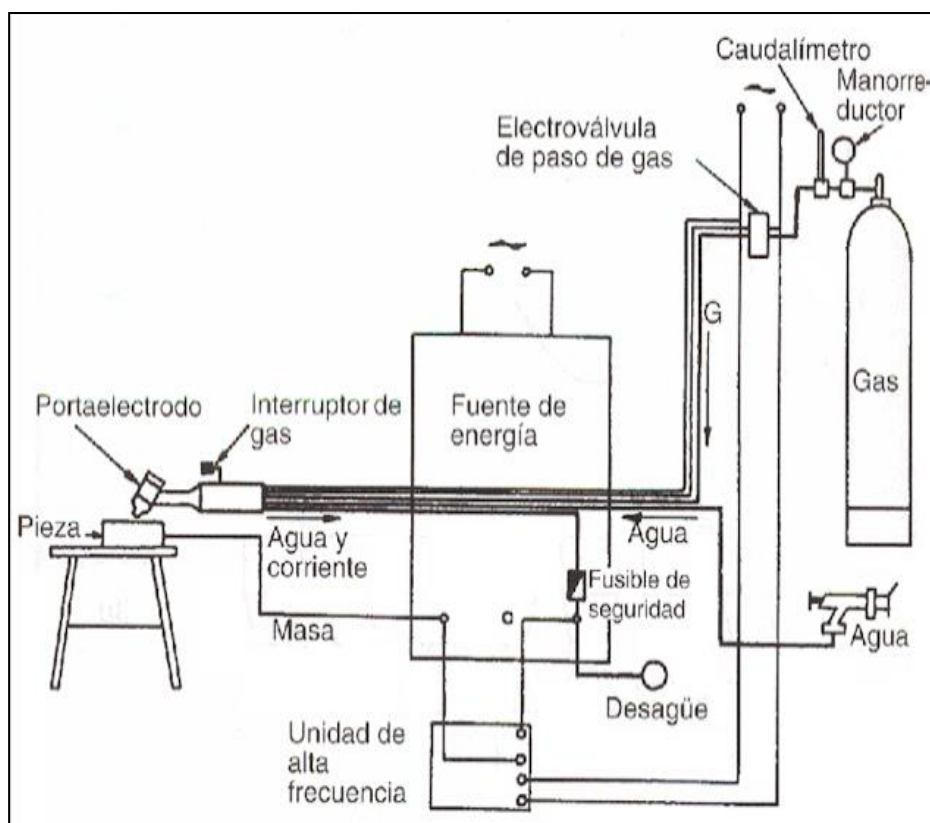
Esquema componentes que forman el equipo de soldeo TIG. Fuente: Ingenieriamecanicaymaas.com
